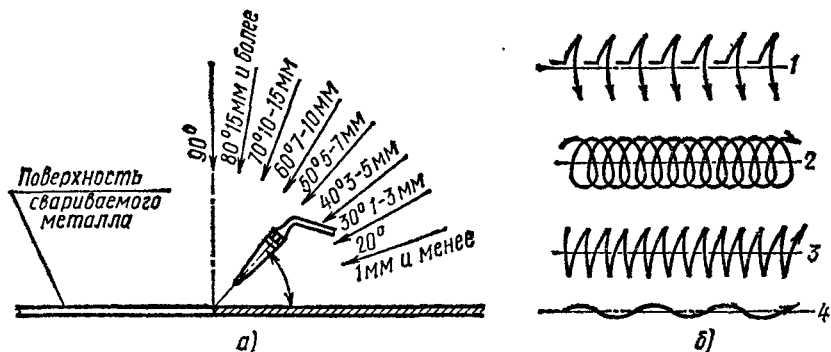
Углы наклона мундштука горелки при сварке различных толщин (а) и способы перемещения мундштука горелки (б):
